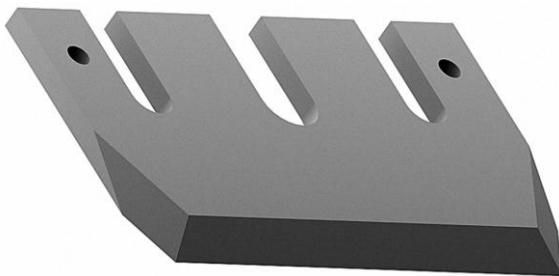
Режущий инструмент малоножевой торцово-конической фрезы
